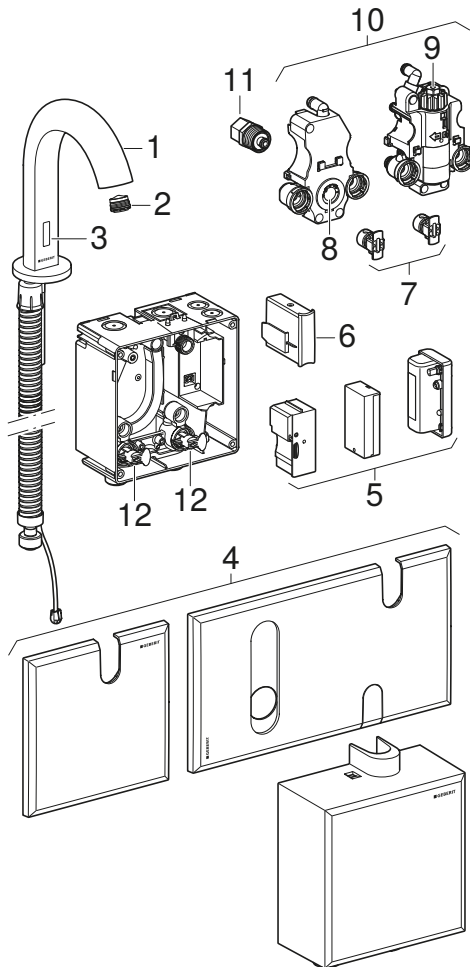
Torneiras de lavatório Geberit Piave e Brenta, instalação em bancada
